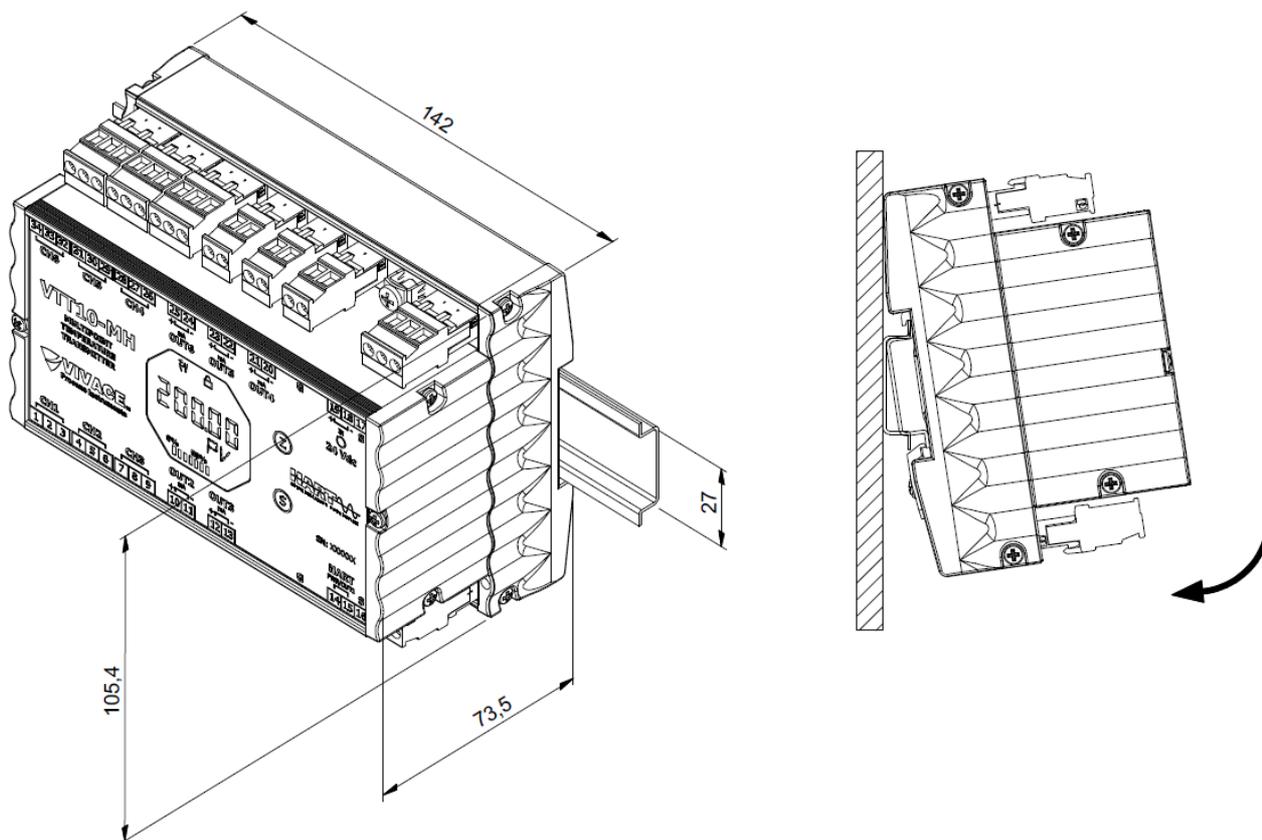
Desenho dimensional e esquema de montagem do VTT10-MH.
